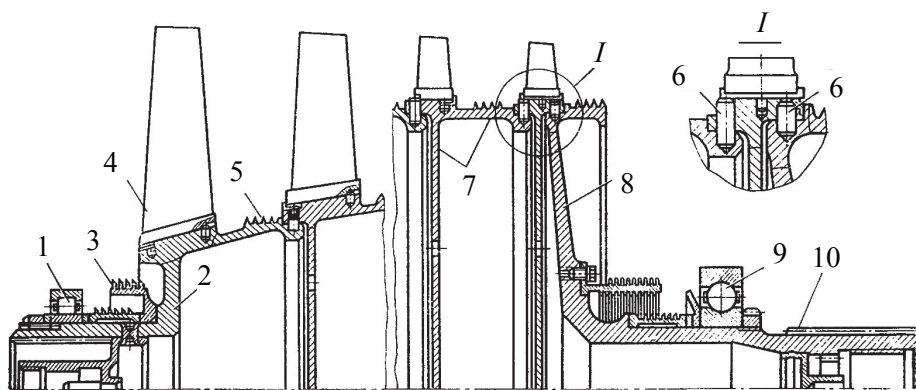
Ротор барабанно-дискового типа с соединением секций напрессовкой и фиксацией штифтами:
